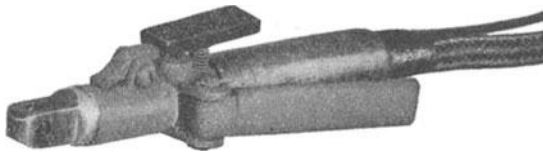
Schweißkolben mit Zündkontakt.
